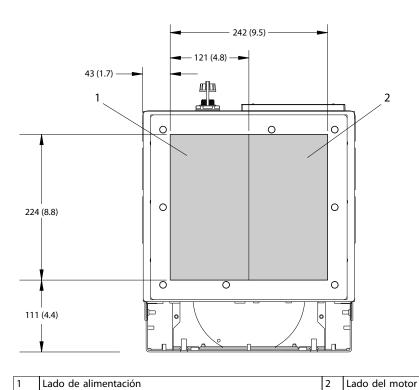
Dimensiones de la placa prensacables del D6h
